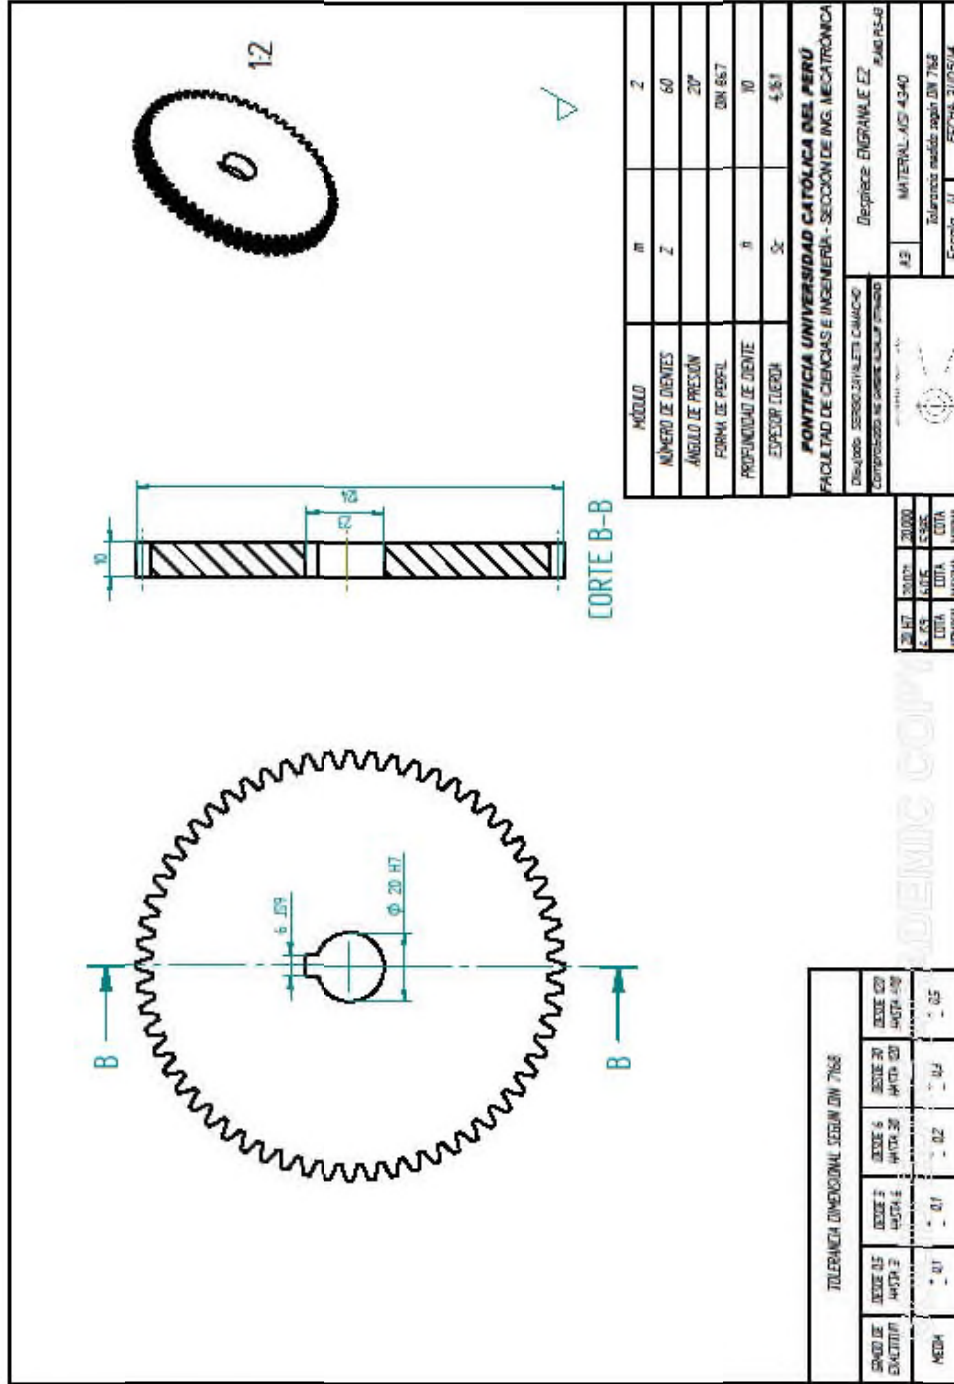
Plano de despiece del engranaje E2. Fuente: Elaboración propia
